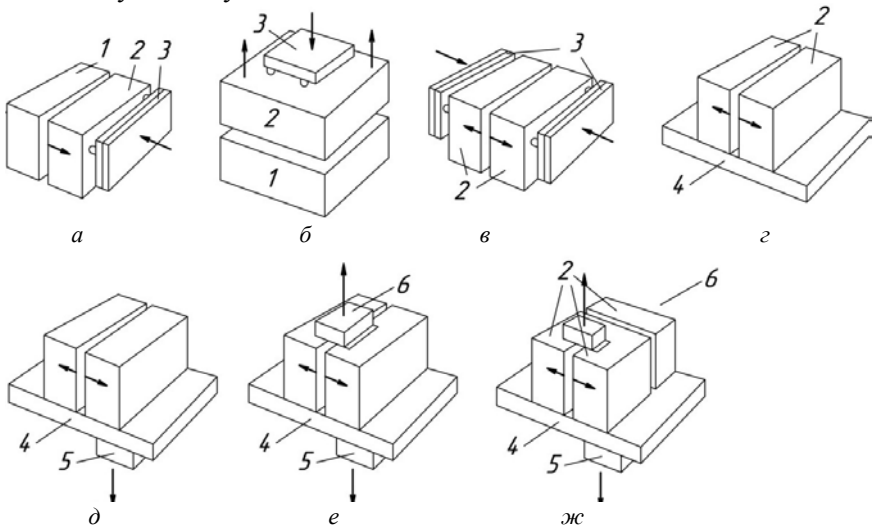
Типы кокилей для универсальных кокильных машин (стрелки – направление движения деталей кокиля):
